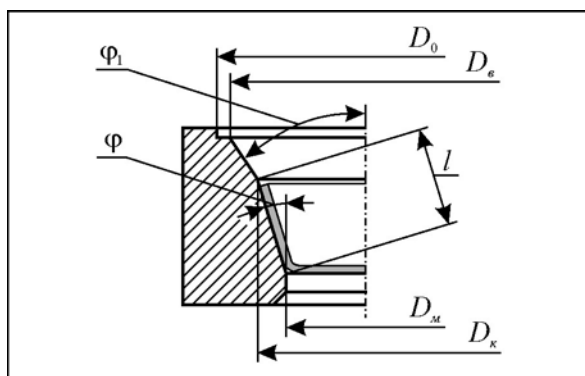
Двоконусна матриця для витягування без притиску заготовки
